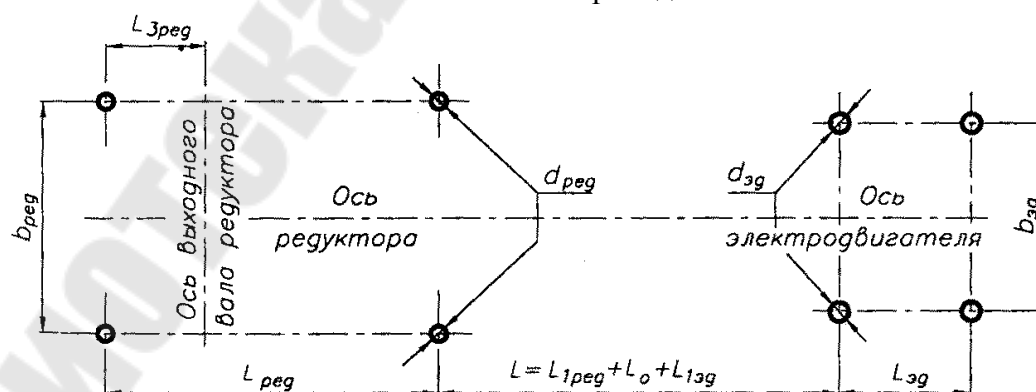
Схема расположения болтов крепления электродвигателя и редуктора к раме
